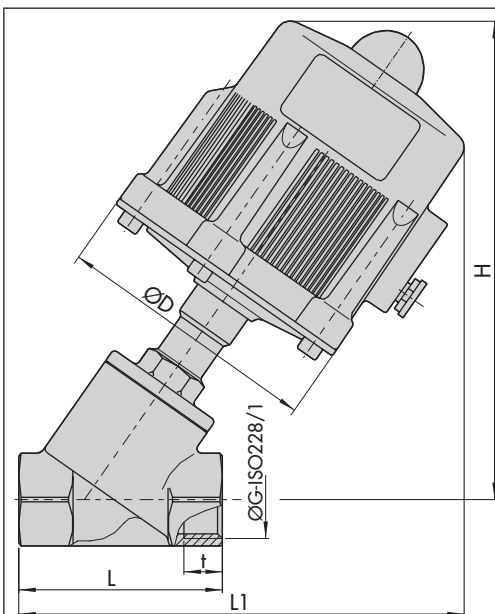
Schrägsitzventil Typ 3353 mit Innengewinde
